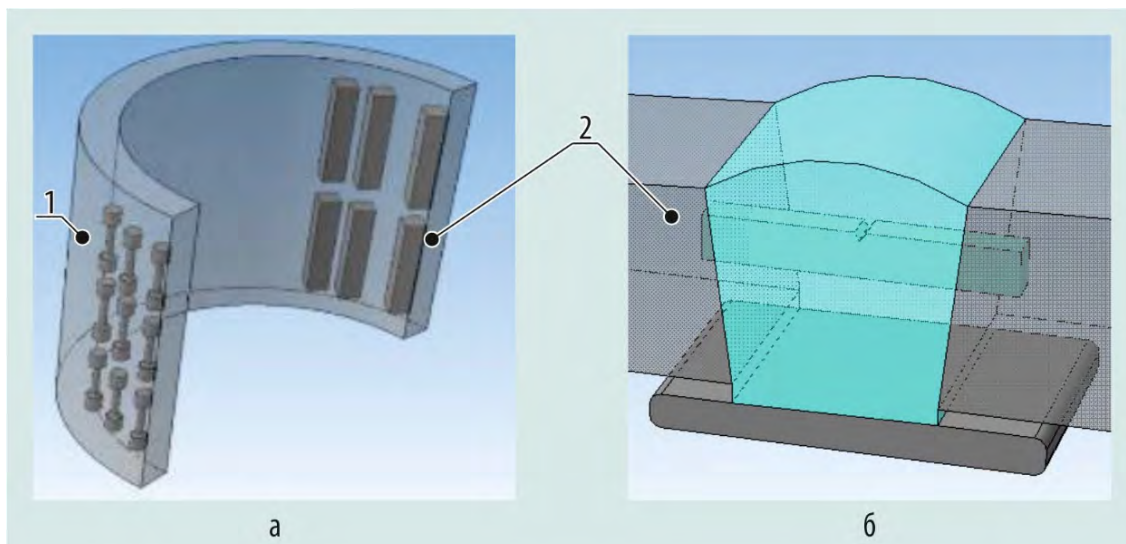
Схема вырезки образцов для механических испытаний на растяжение (1) и на ударную вязкость (2) из основного металла паропровода (а) и из сварного соединения (б)
